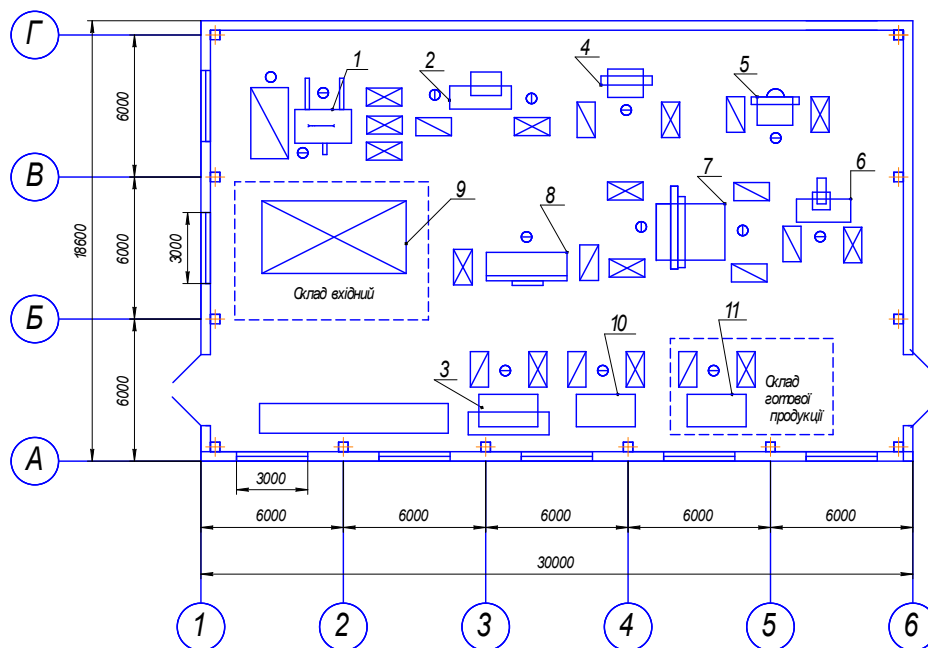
Варіант другий : планування обладнання з виготовлення спинок ЛДЗКМС — рамка виготовляється з заготовок, а вставка — зі брусків
